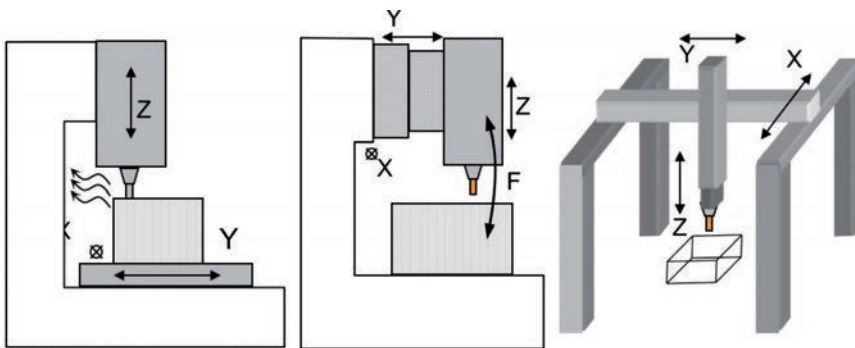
Tres tipos de estructuras. a) Columna fija tipo C. b) Columna móvil tipo C.
